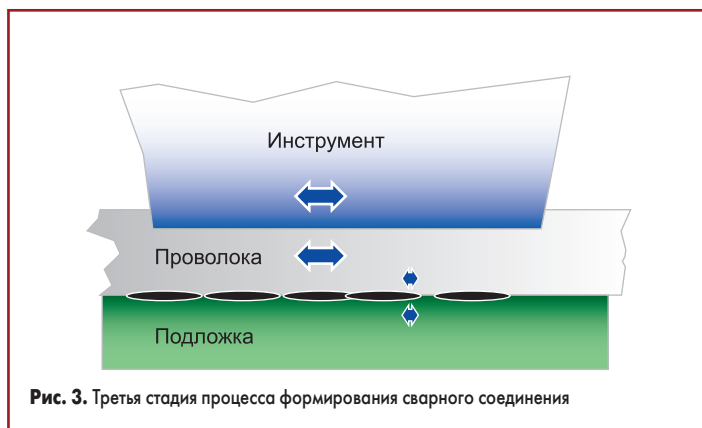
Третья стадия процесса формирования сварного соединения
